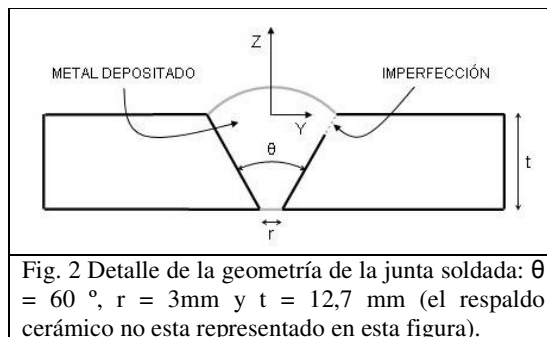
Detalle de la geometría de la junta soldada: $\theta = 60^\circ$, $r = 3\text{mm}$ y $t = 12,7\text{mm}$ (el respaldo cerámico no está representado en esta figura).
